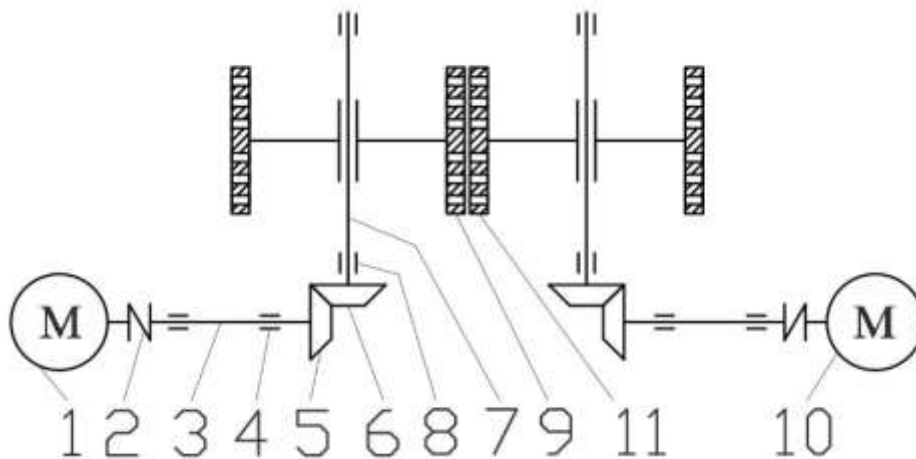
Кінематична схема двувальцевої дробарки.
